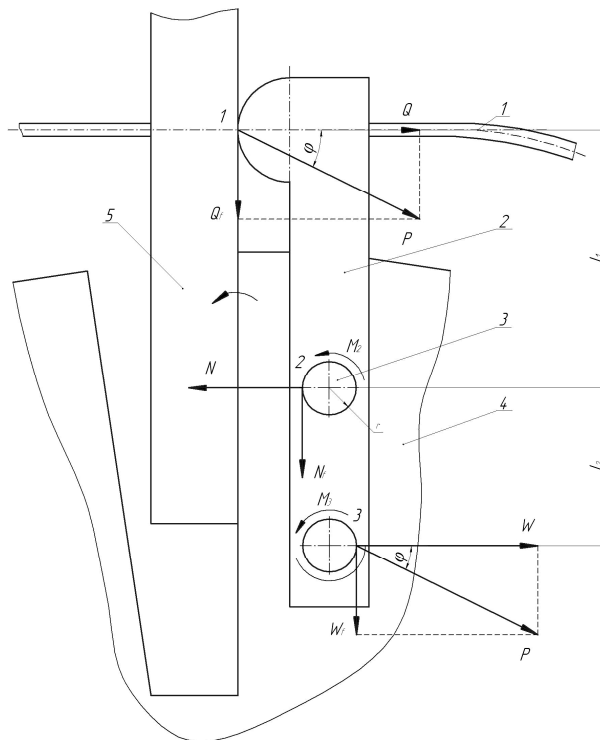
Розрахункова схема для визначення зусиль, які діють на ланку привода гнучкого канатного конвеєра: 1 – канат; 2 – Г-подібний штовхач; 3 – заклепки; 4 – привідний диск; 5 – подавальний диск
